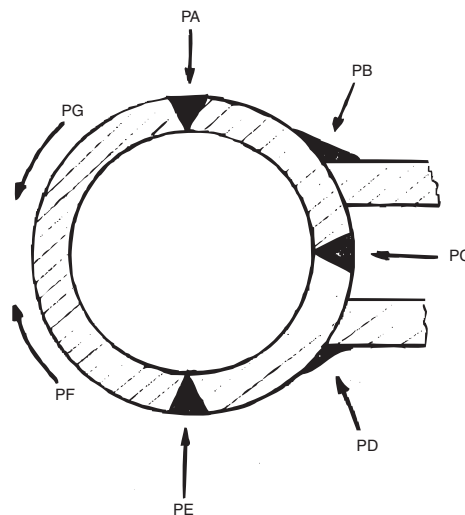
Позиции при сварке согласно ISO 6947
